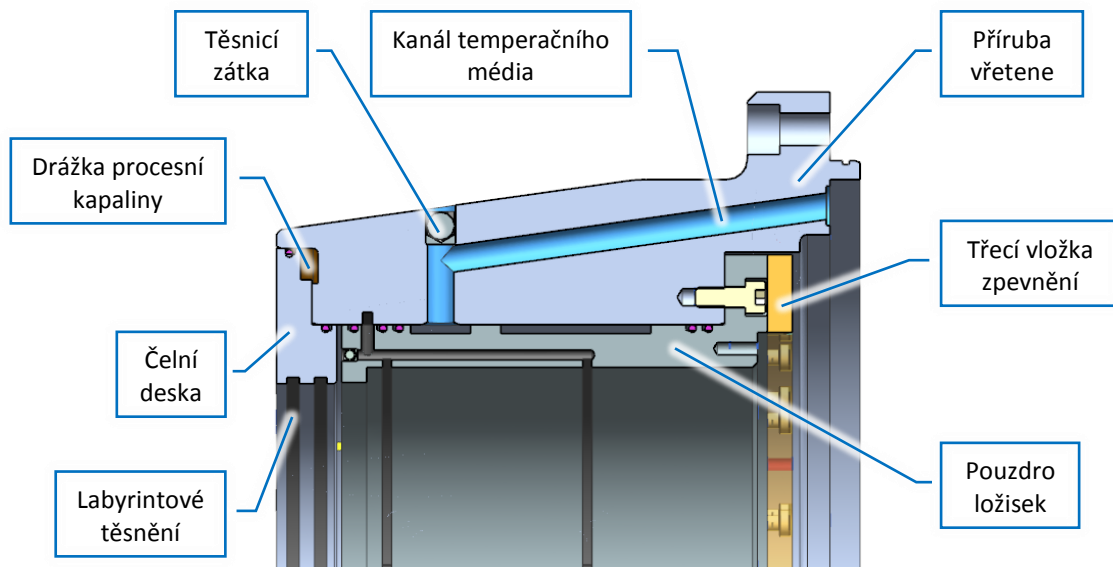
ISO pohled na konstrukční uzel rotoru vřetene
